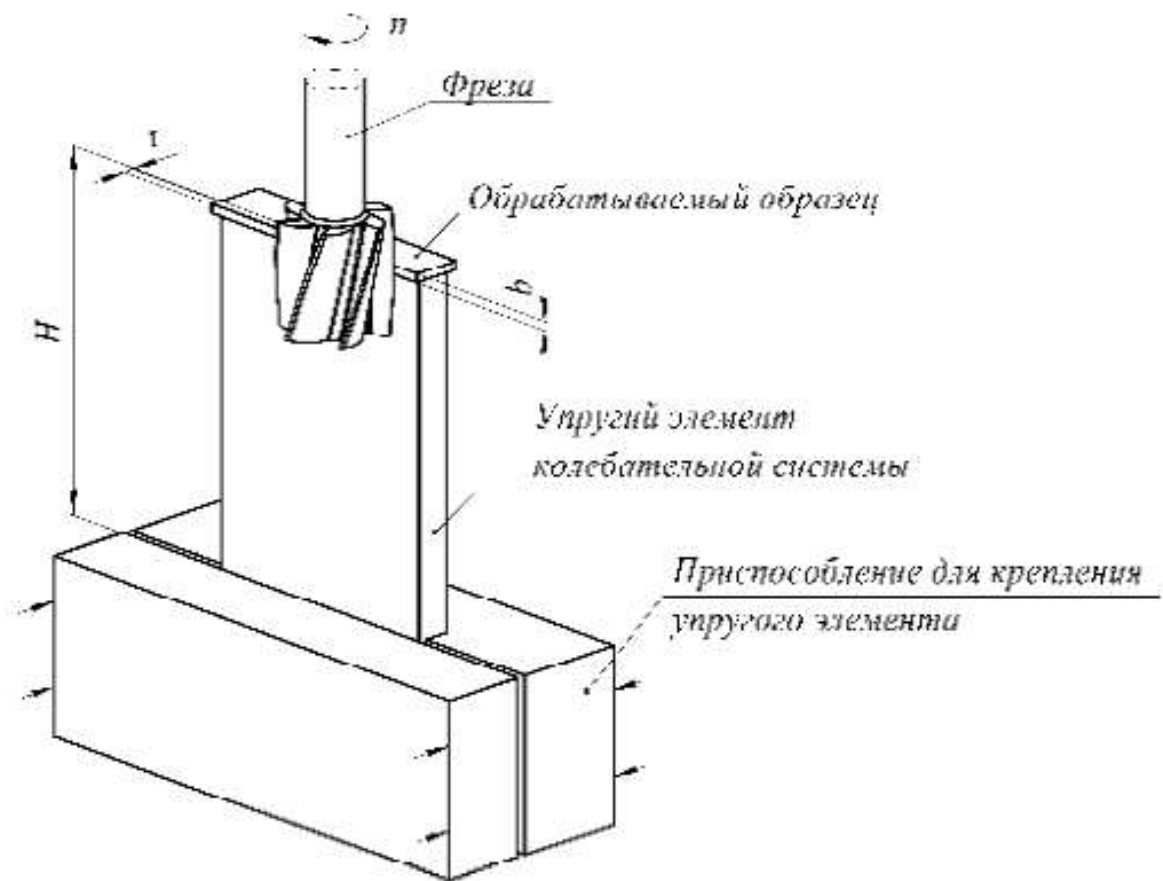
Схема оброблення нежорсткої деталі
